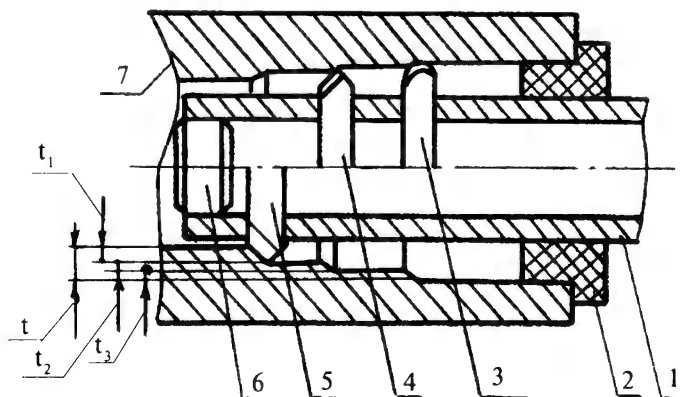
Трехрезцовая расточная головка с двухсторонним расположением резцов: 1 - корпус головки, 2 - шпонка, 3 - чистовой резец, 4 - получистовой резец, 5 - черновой резец, 6 - пробка, 7 - обрабатываемая деталь
